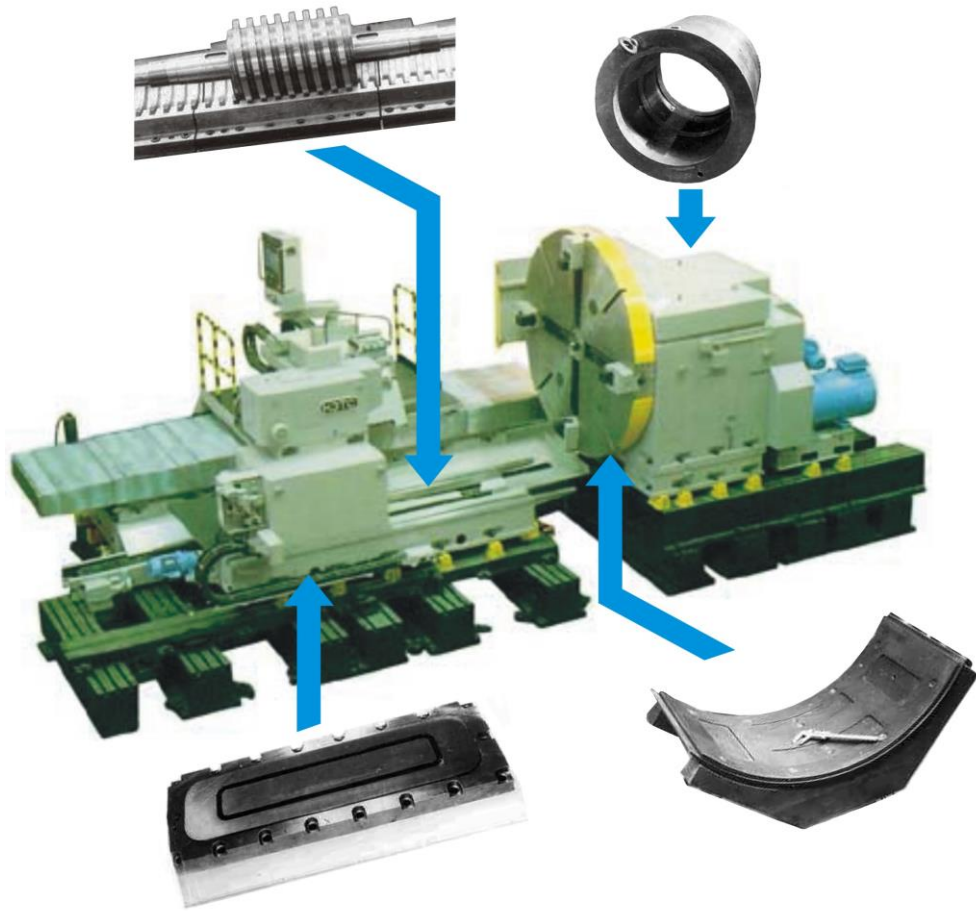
Опори й передачі рідинного тертя для токарного верстата
